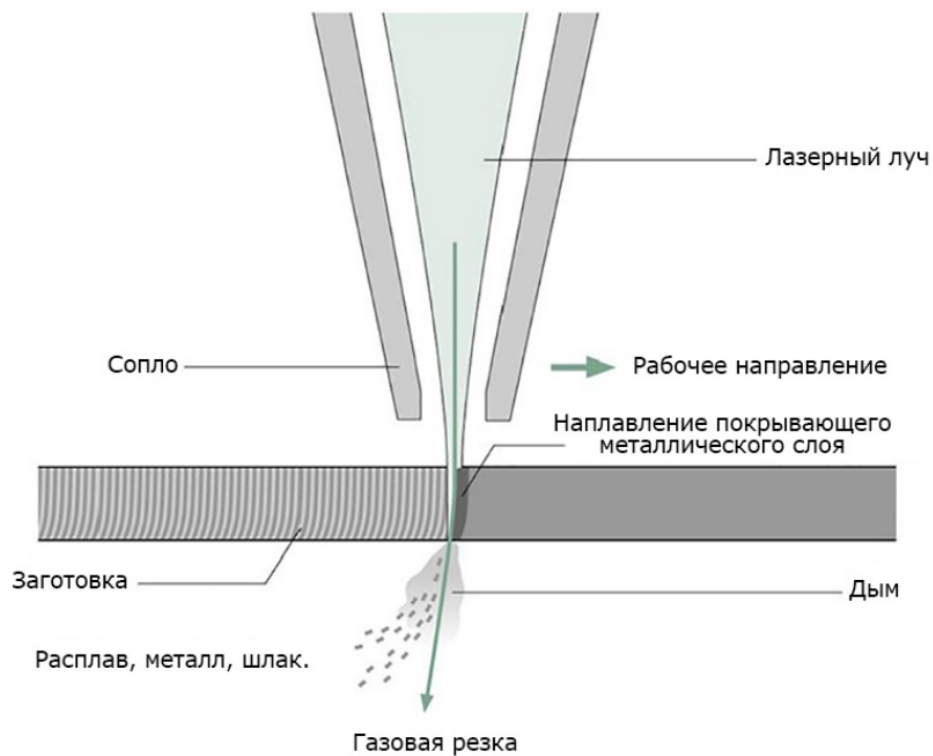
Газовая резка. (лазерный луч плавит заготовку, а ржущий газ сдувает расплавленный материал и шлак в зоне разреза)
